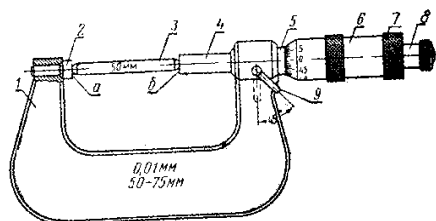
Микрометр для наружных измерений: 1 – скоба; 2 – жесткая пятка; 3 – калибр (концевая мера) для установки микрометра на нуль; 4 – подвижная пятка (микровинт); 5 – стержень; 6 – микрометрическая головка; 7 – установочный колпачок; 8 – трещоточное устройство; 9 – тормозной приспособление
